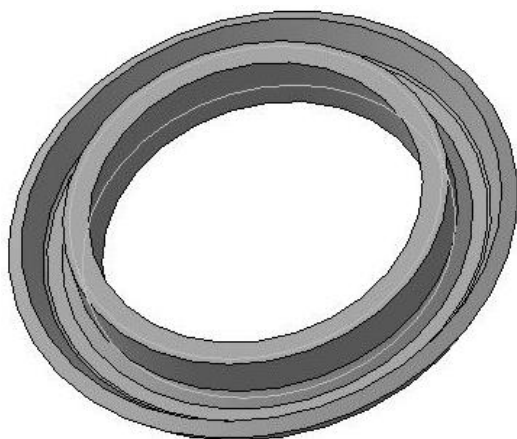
Загальний вид та типові дефекти деталі "Фланець"
